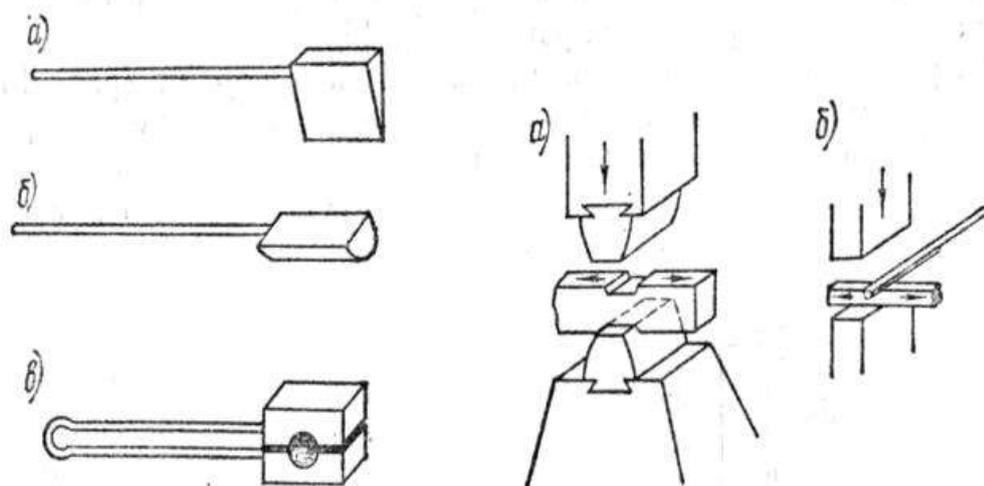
Схема свободной ковки: а-топор; б-раскатка; в-обжимка
